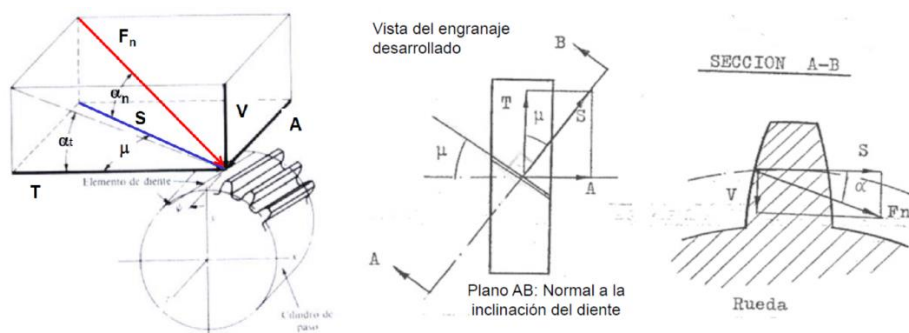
Esquema de cargas generadas en engranajes cilíndricos helicoidales.
